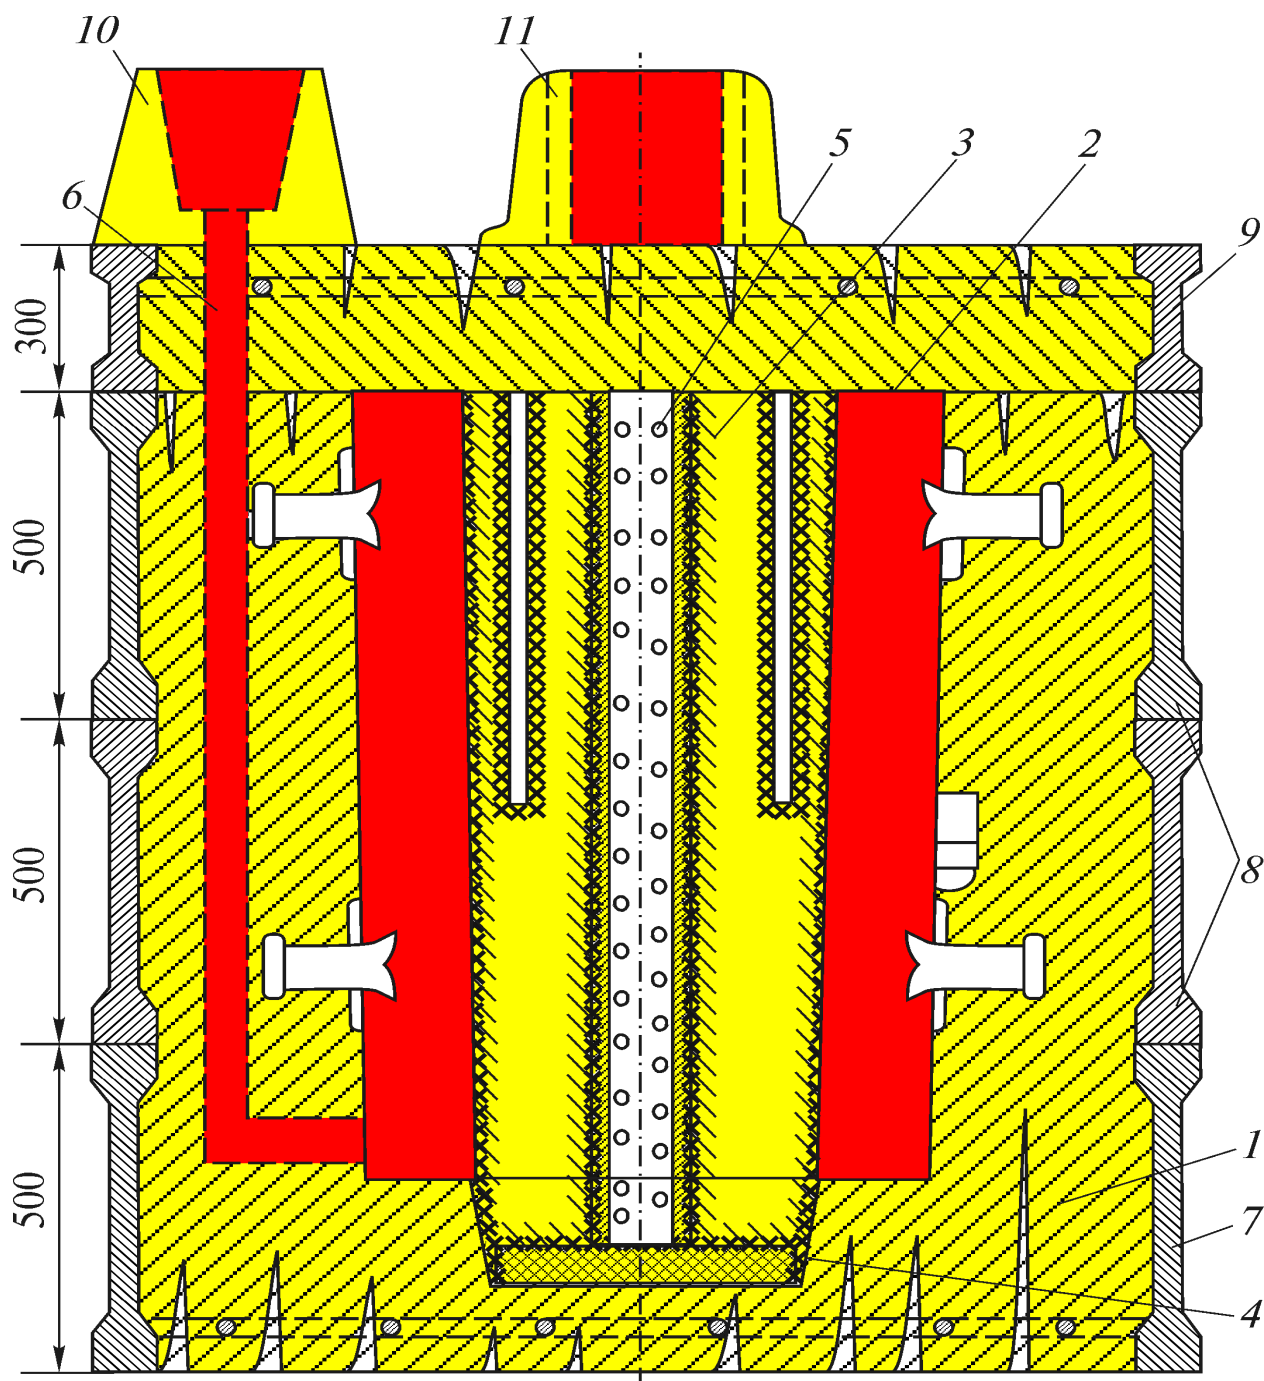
Схема ливарної форми для ковальської виливниці:
